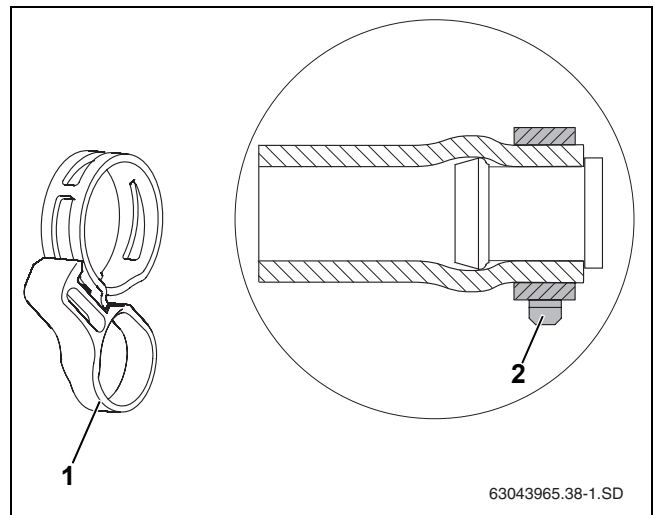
Abrazadera con anillo tensor montada sobre el caperuza de cierre previamente montado
